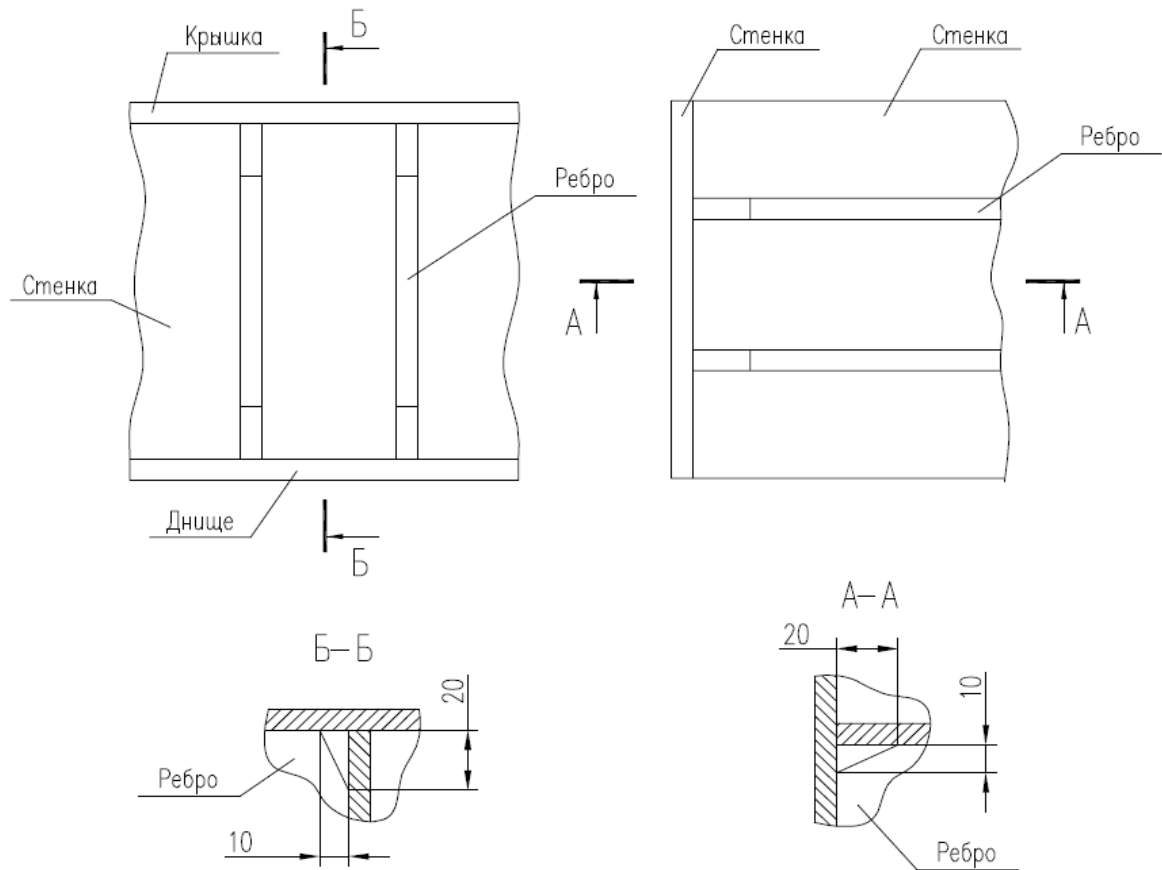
Установка и прихватка рёбер к стенкам, днищу и крышке бака
